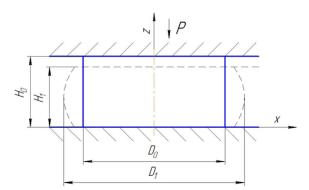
Схема осадки: H0, D0 - начальные размеры заготовки, H1, D1 - размеры заготовки после осадки
